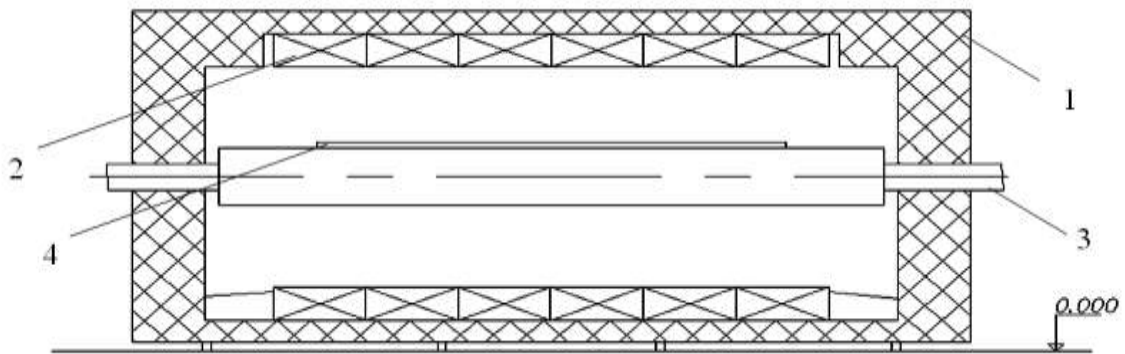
Общая конструкция печи отжига: 1 – корпус с теплоизолирующей каолиновой ватой; 2 – прямоугольные короба с охлаждающим воздухом; 3 – металлические валы; 4 – лента стекла
